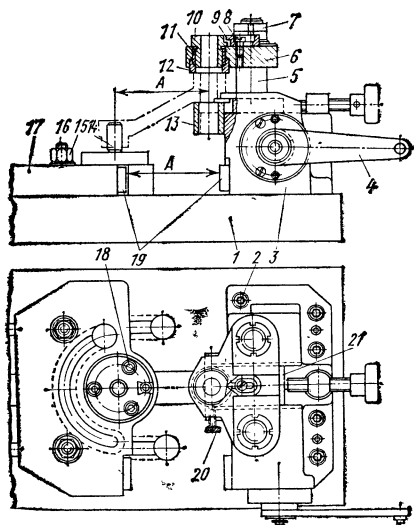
Переналаживаемый кондуктор для обработки второго отверстия в бобышке рычага
